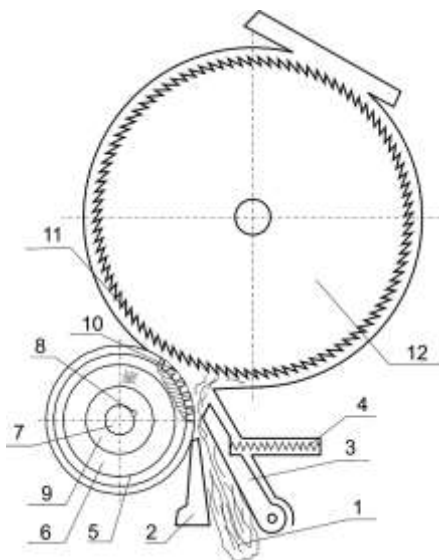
Зон питания пневмомеханического прядильного устройства: 1-лента; 2- уплотнительная воронка; 3-столик; 4-пружина; 5-питающий цилиндр; 6- втулка; 7-вал; 8-шпонка; 9-внутренняя втулка; 10-рифля; 11-зубь; 12-дискретизирующий барабанчик
